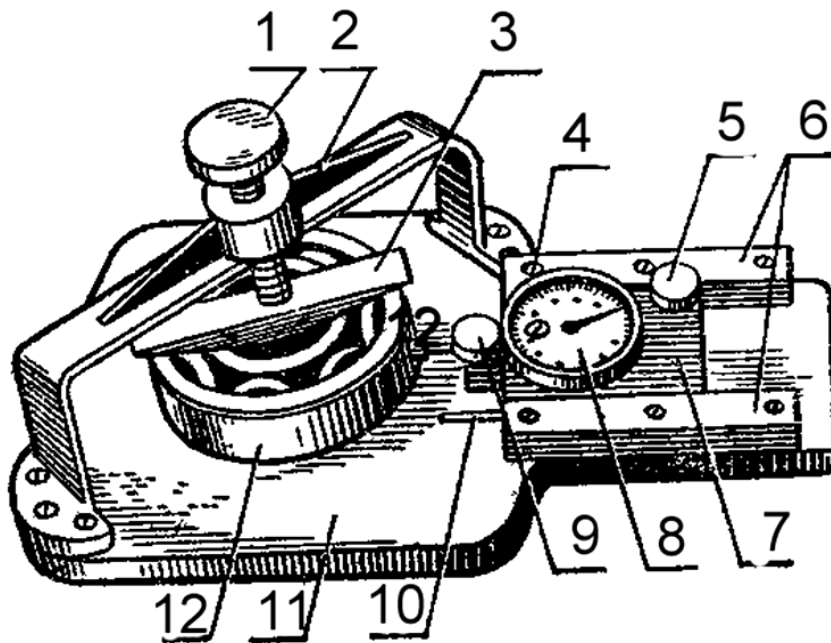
Індикаторний прилад для перевірки радіальних зазорів у підшипниках кочення: 1, 4 і 9 – гвинти; 2 – міст; 3 – конус; 5 – гвинтовий затискач; 6 – напрямні; 7 – каретка; 8 – індикатор годинникового типу; 10 – паз; 11 – плита; 12 – підшипник
